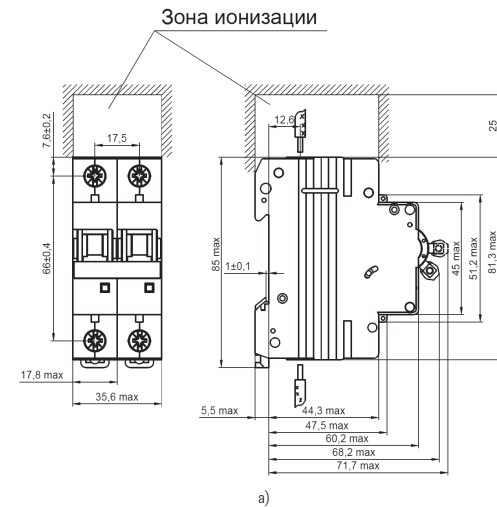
Габаритные и установочные размеры выключателей на постоянный ток
